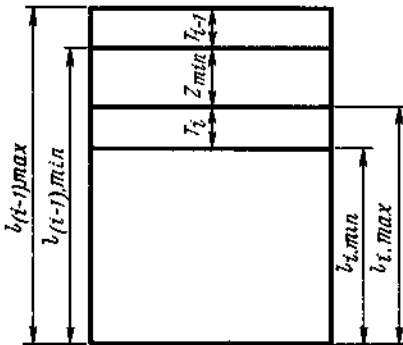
Схема обработки заготовки при методе пробных проходов и промеров
